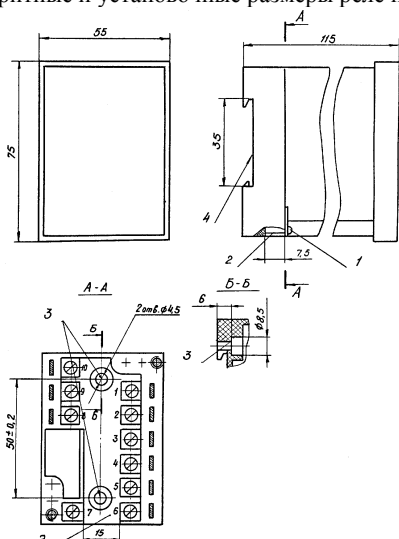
Габаритные, установочные, присоединительные размеры реле (выступающий монтаж реле для крепления на плоскость или рейку):
